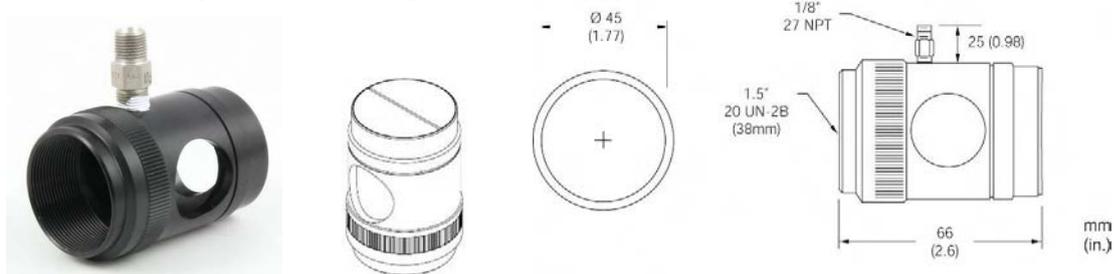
Vue et dimensions du miroir de visée à 90° (E-RA)
